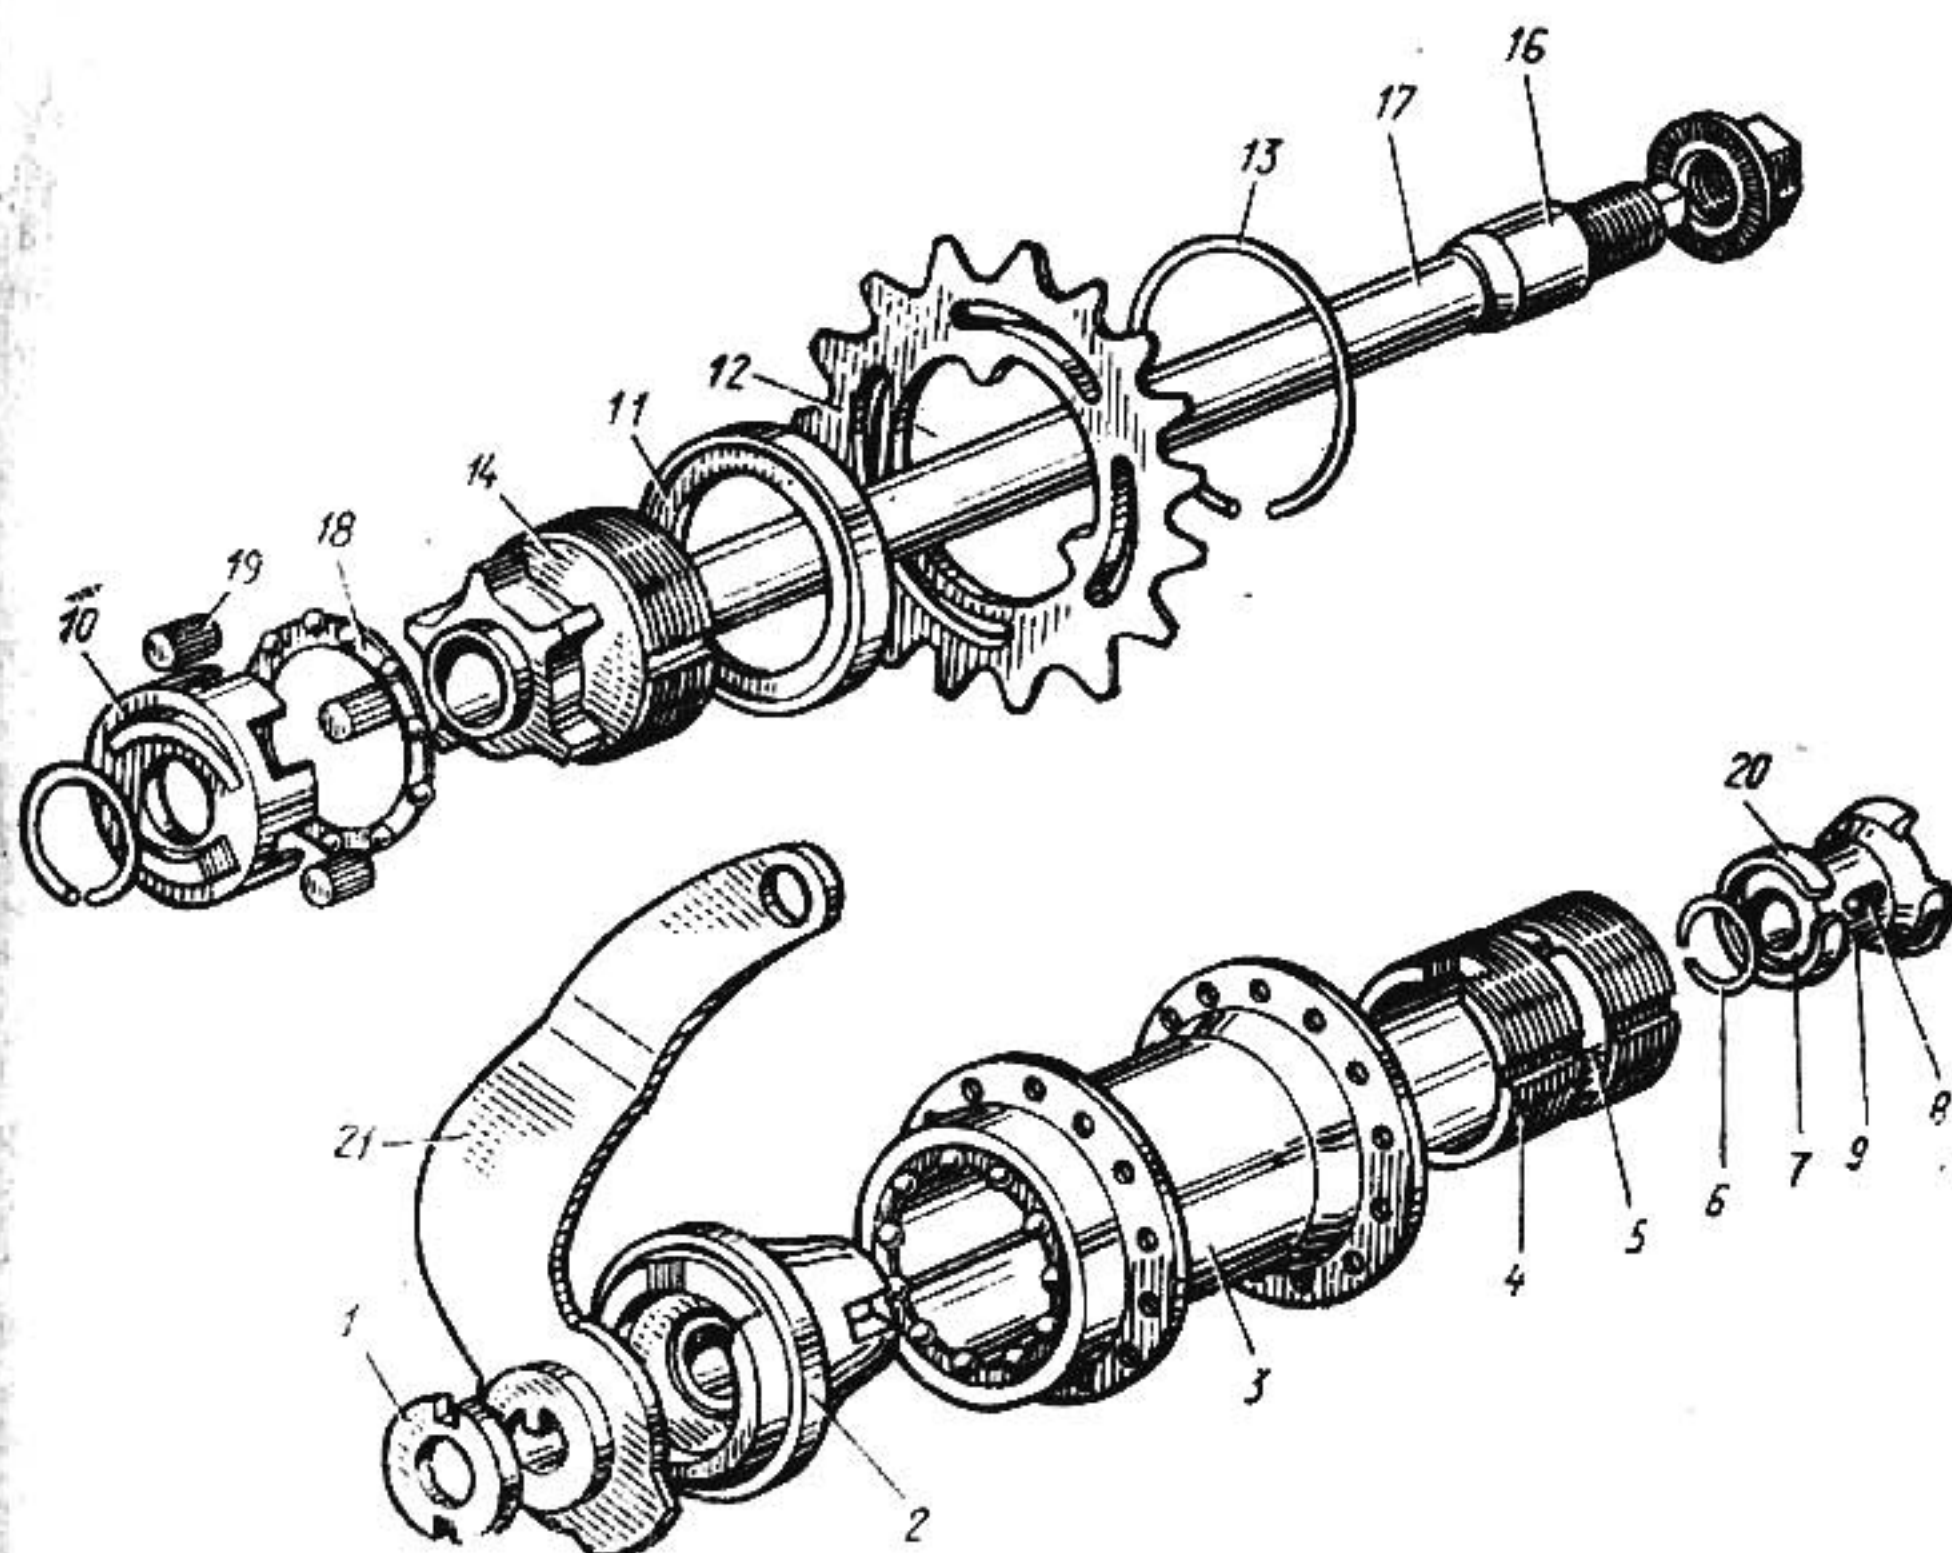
Детали втулки заднего колеса типа «Торпедо»:
